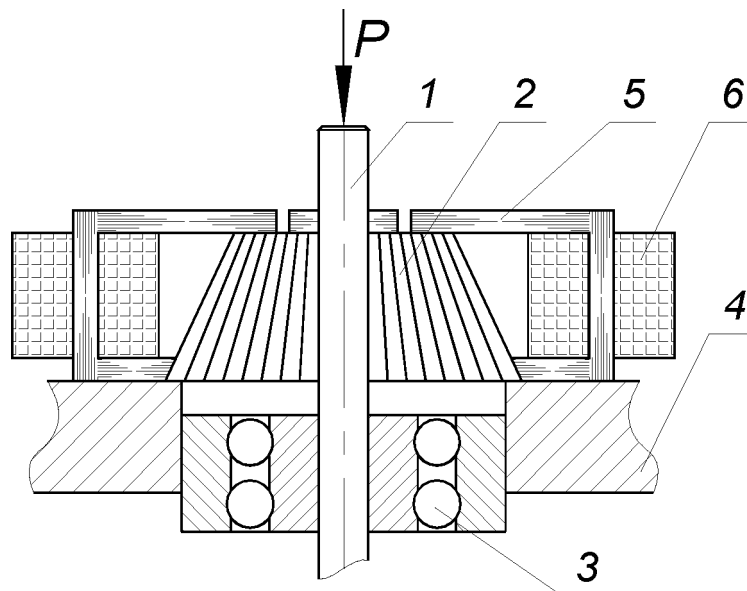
Установка ТПЧ для разборки узла вал-шестерня-подшипник
